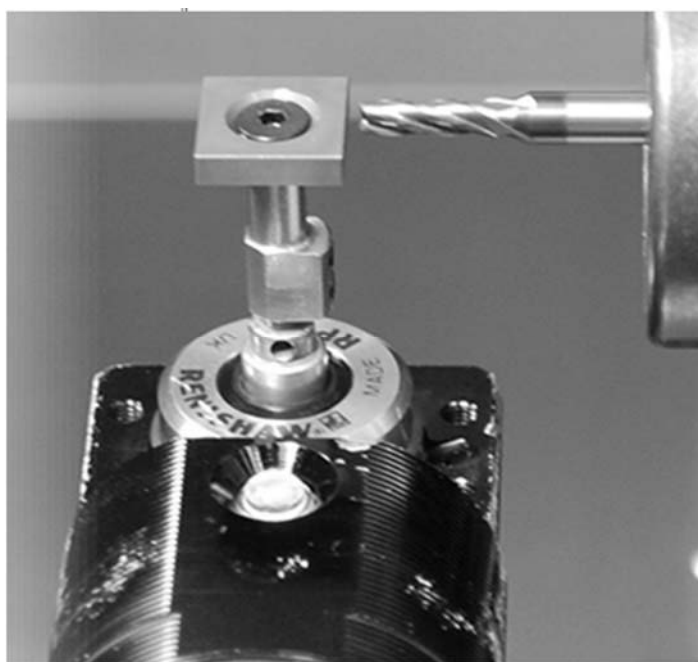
Местный вид приспособления Renishaw серии HPR для наладки фрезы
